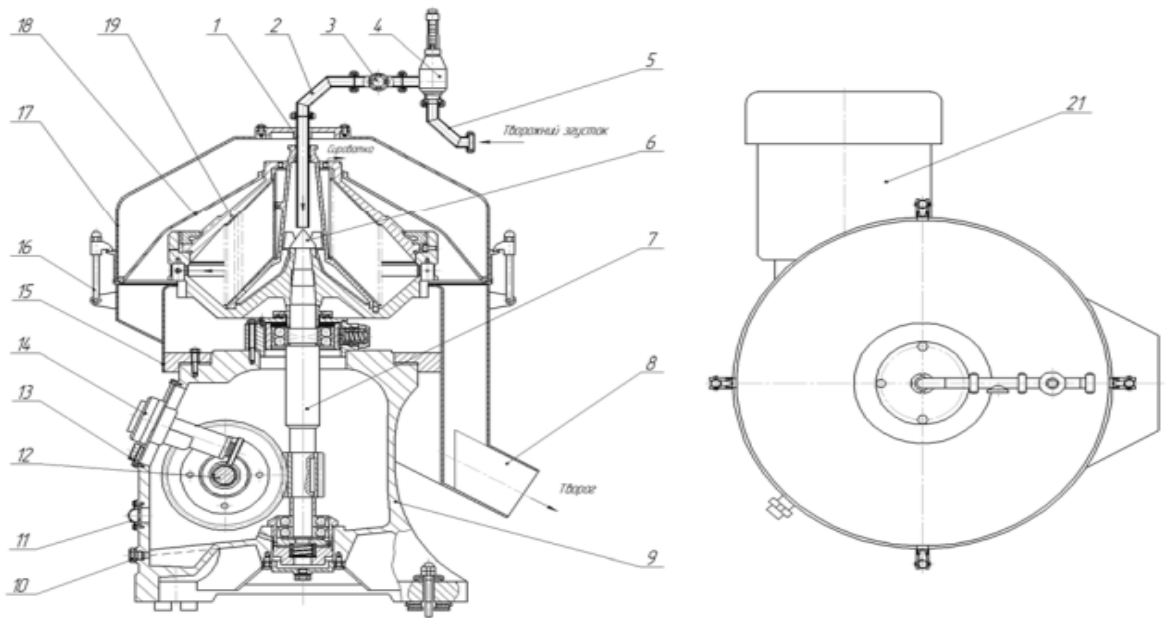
Сепаратор ОСЯ: 1 - живильний патрубок; 2 – коліно; 3 - оглядове вікно; 4 – ротаметр; 5 – коліно; 6 - гайка веретена; 7 - вертикальний вал; 8 – лоток; 9 – станина; 10,13 – пробки; 11 – масло-показчик; 12 - горизонтальний вал; 14 – тахометр; 15 - чаша станини; 16 – прижим; 17 – кришка; 18 - приймач сироватки; 19 - барабан; 20 – патрубок; 21 – електродвигун
